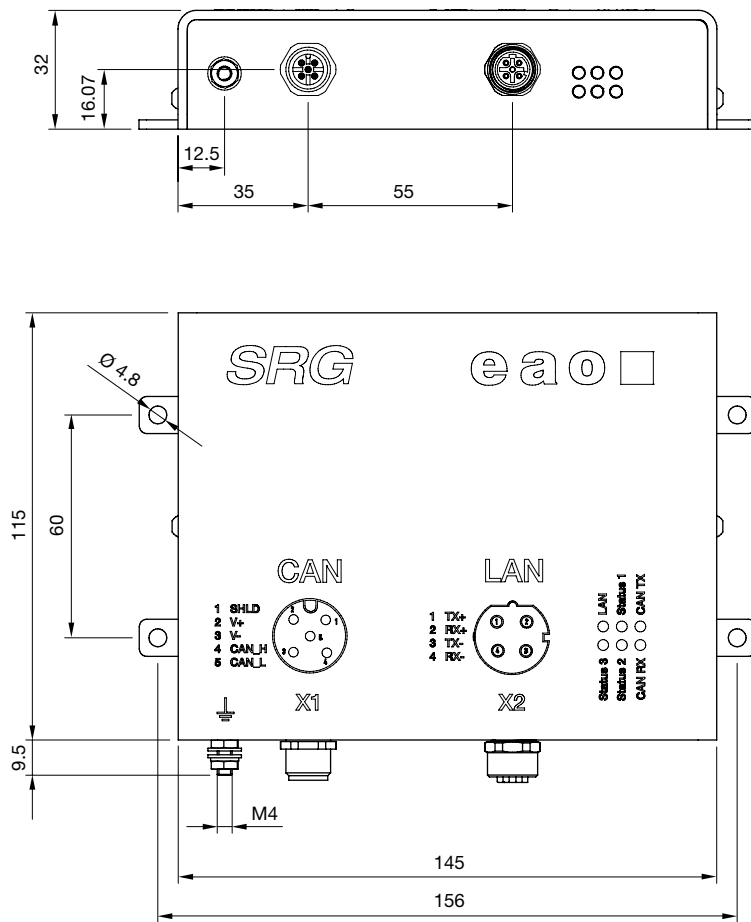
Abmessungen (mm) Gehäuse Gateway (SRG).
